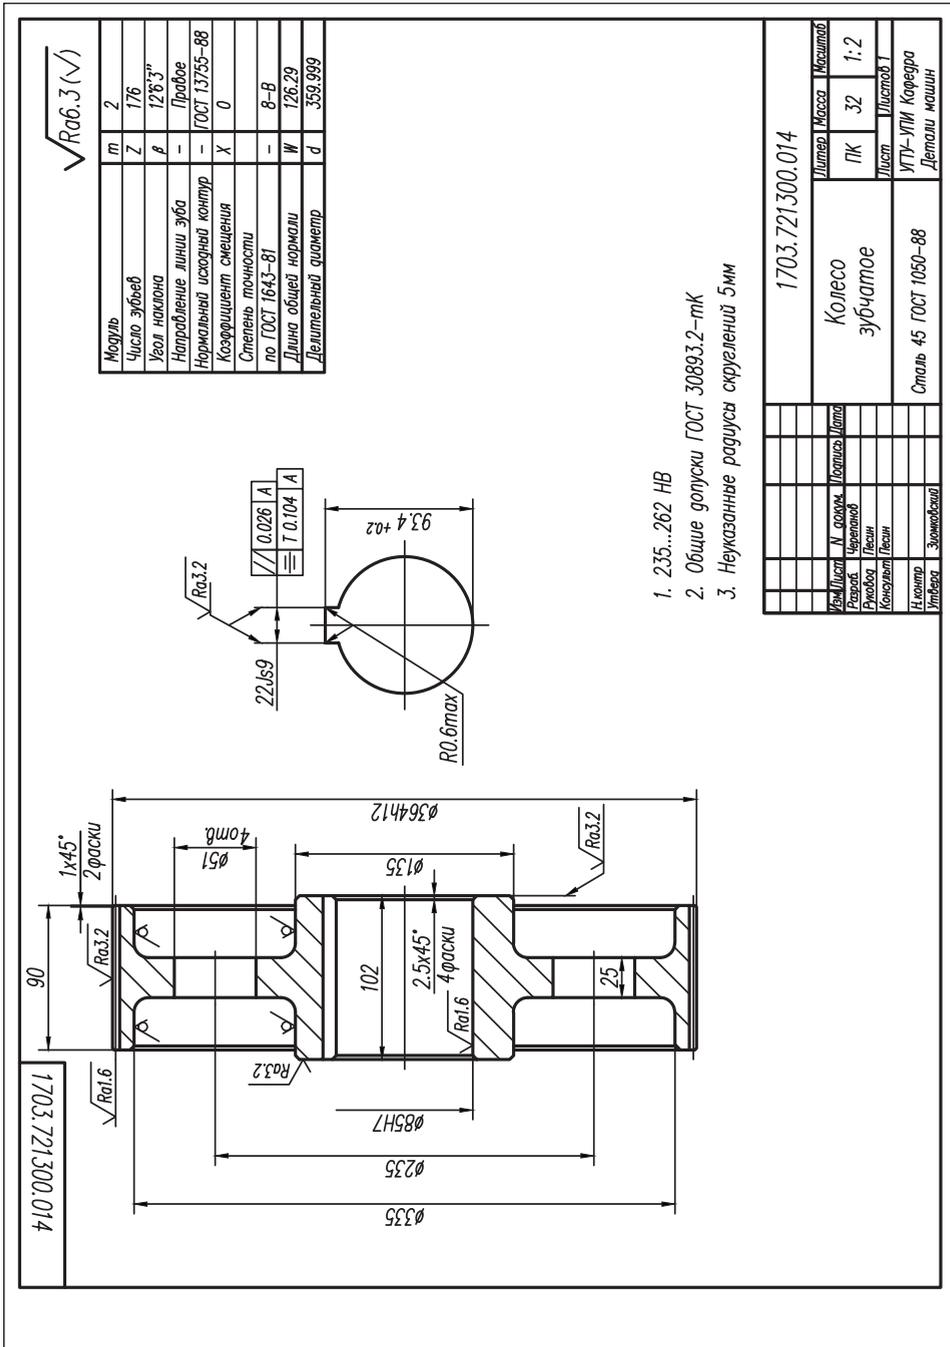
Рабочий чертеж зубчатого цилиндрического колеса
